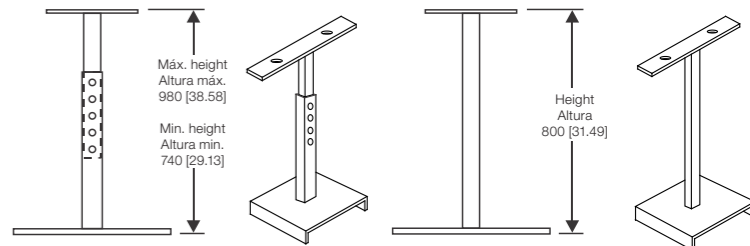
Pedestal adjustable and fixed - Dimensiones in millimeters [inches]
